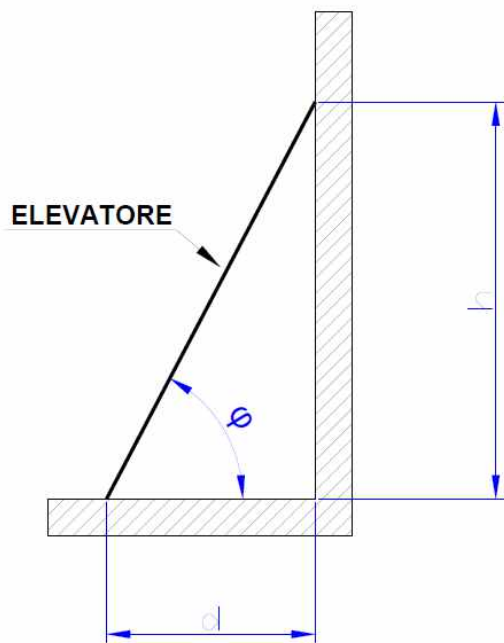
DIMENSIONI FONDAMENTALI PER MONTAGGIO ELEVATORE
